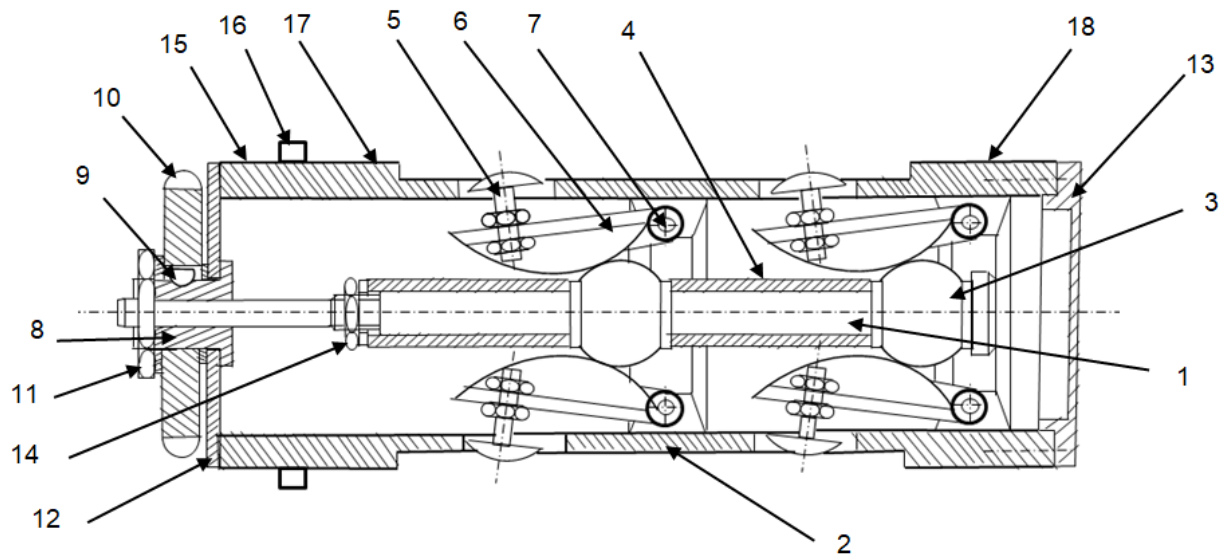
Coupe longitudinale du dispositif conçu en situation d'usinage d'un bout de tube
